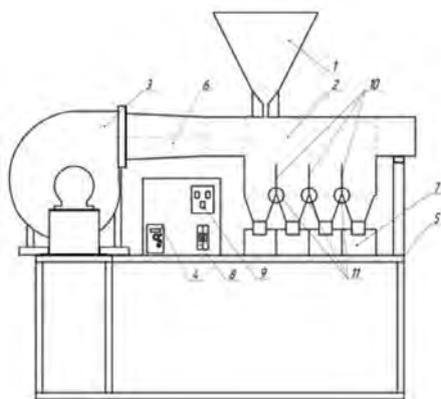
Пневматический сепаратор (расшифровка обозначений в тексте)
